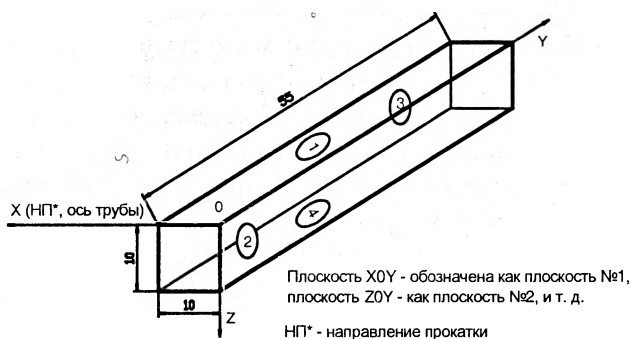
Схема нумерации исследуемых поверхностей образца
